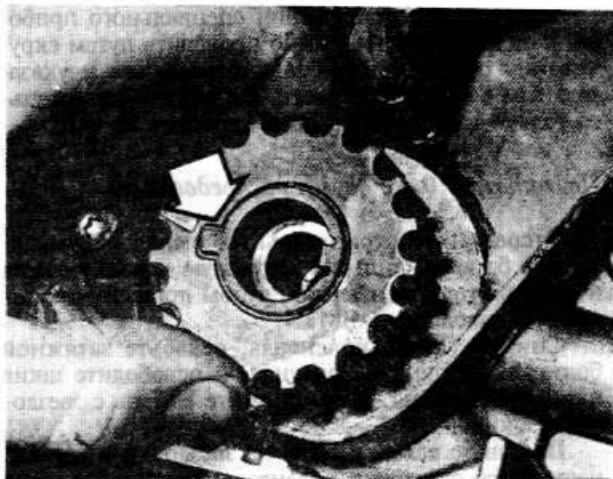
Установка шкива коленвала с фланцем и фиксирующей бобышкой (указана стрелкой)
